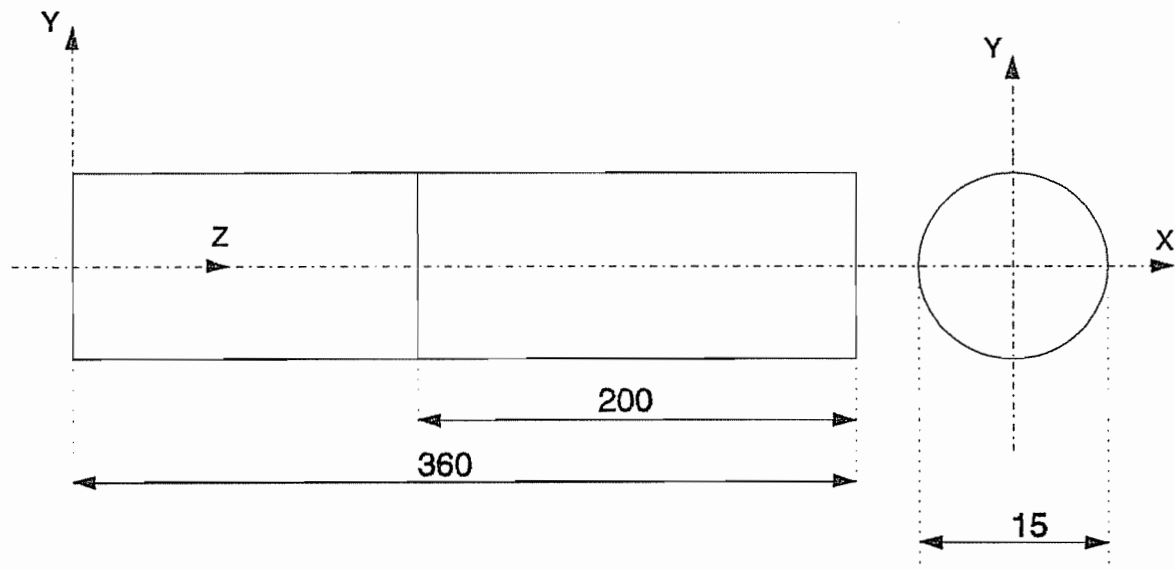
Géométrie et axes de l'éprouvette cylindrique
